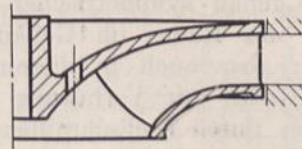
Francisturbinenrad für geringe Laufgeschwindigkeit.
